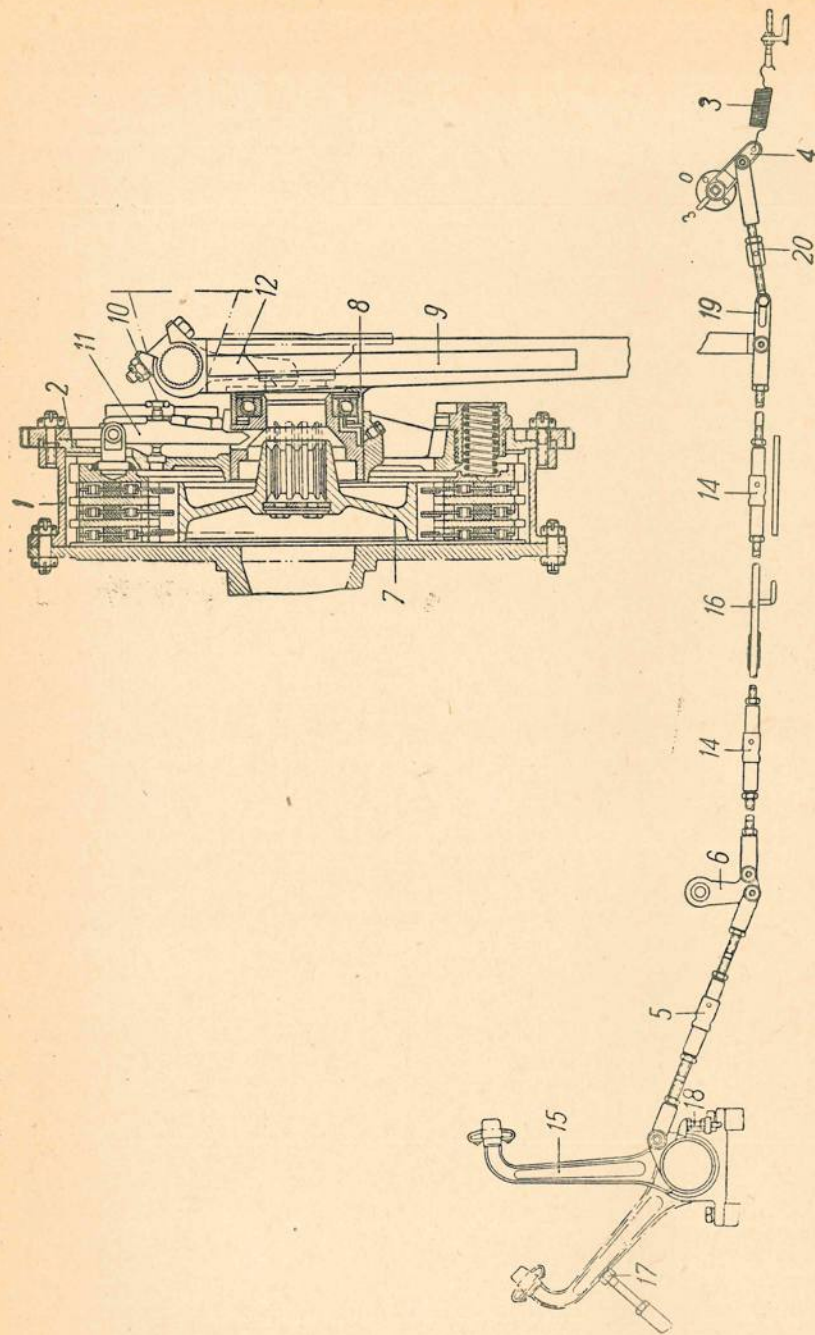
Схема привода управления главного фрикциона и тяг замка коробки перемены передач: 1 — наружный барабан; 7 — ведомый барабан; 9 — выжимные рычаги; 10 — регулировочные болты; 11 — регулировочная муфта; 14 — стяжные муфты; 15 — стержень педали главного сцепления; 16 — тяга главного сцепления; 17 — болт упора педали главного сцепления; 18 — регулировочный болт упора педали; 19 — выжимные рычаги; 20 — тяга главного фрикциона.
